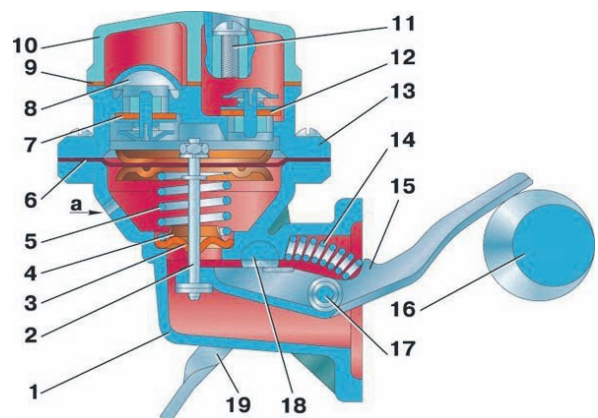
Паливний насос Б9В (451М-1106010-30, 451М-1106010-30): а – контрольний отвір; 1 – корпус; 2 – шток; 3 – ущільнювач; 4 – шайба; 5, 14 – пружини; 6 – діафрагма; 7 – впускний клапан; 8 – фільтр-сітка; 9 – прокладка; 10 – кришка; 11 – гвинт; 12 – випускний клапан; 13 – головка корпусу; 15 – важіль приводу; 16 – ексцентрик розподільного валу; 17 – вісь важеля приводу; 18 – валик важеля ручної підкачки; 19 – важіль ручної підкачки
